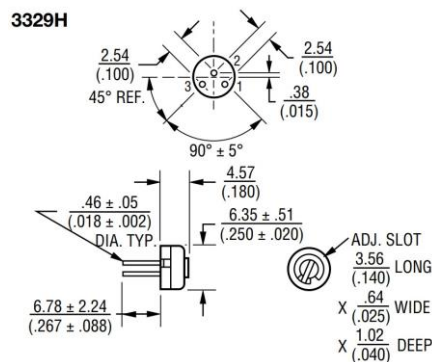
Габаритні розміри резистора підстроювального
